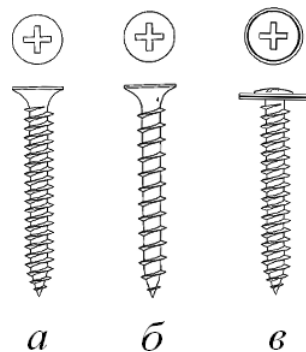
Шурупы-саморезы: а — полимерные материалы—металл; б — по дереву; в — металл—металл
